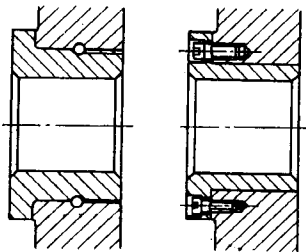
Резьбовые поверхности сборных конструкций.
